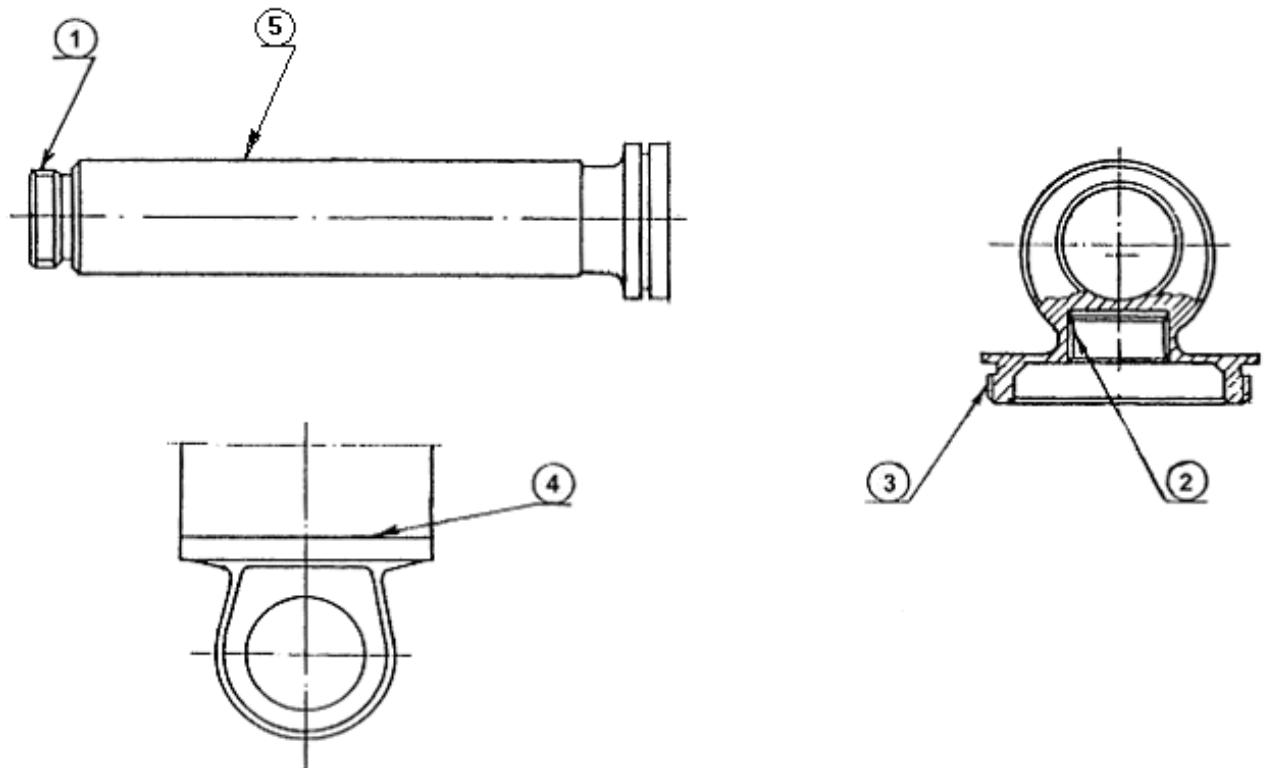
Основные дефекты гидравлического гасителя колебаний, ремонтируемые сваркой или наплавкой
